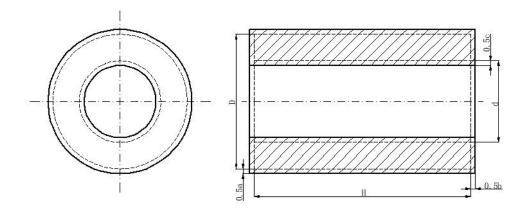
钛合金套筒类锻件机械加工余量与公差
